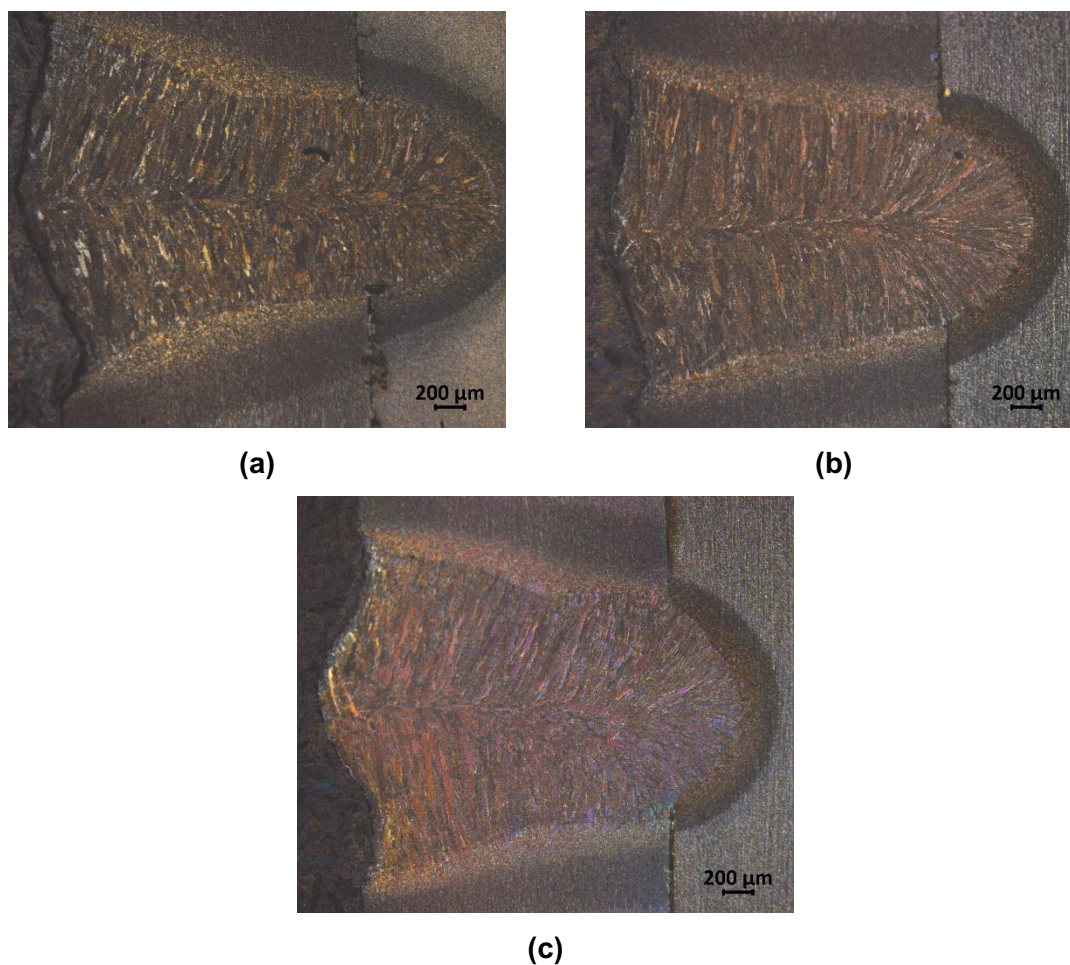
Conjunto P05: (a) Cordão A - SS; (b) Cordão A - 180; (c) Cordão C – SS.
